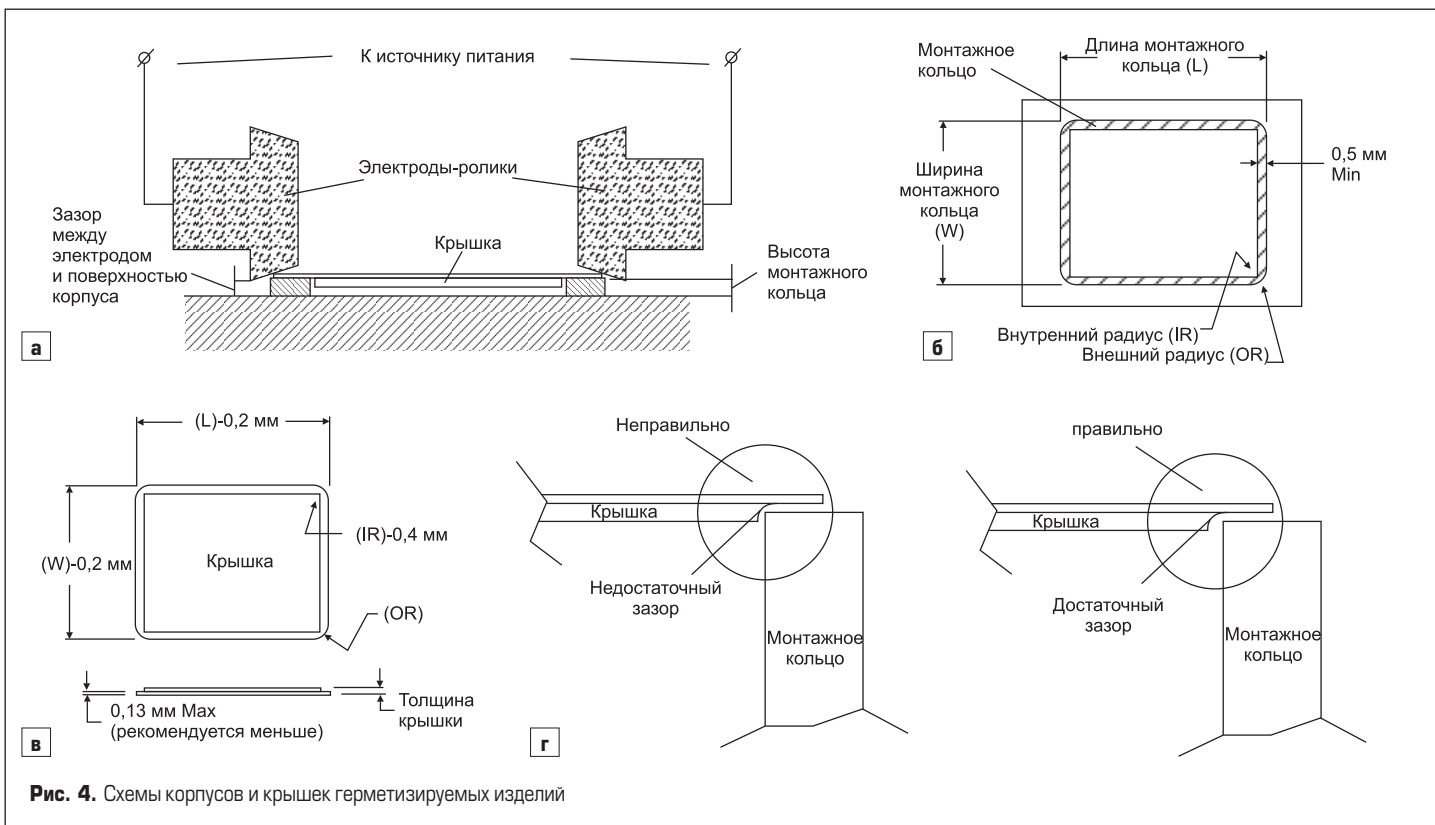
Схемы корпусов и крышек герметизируемых изделий
